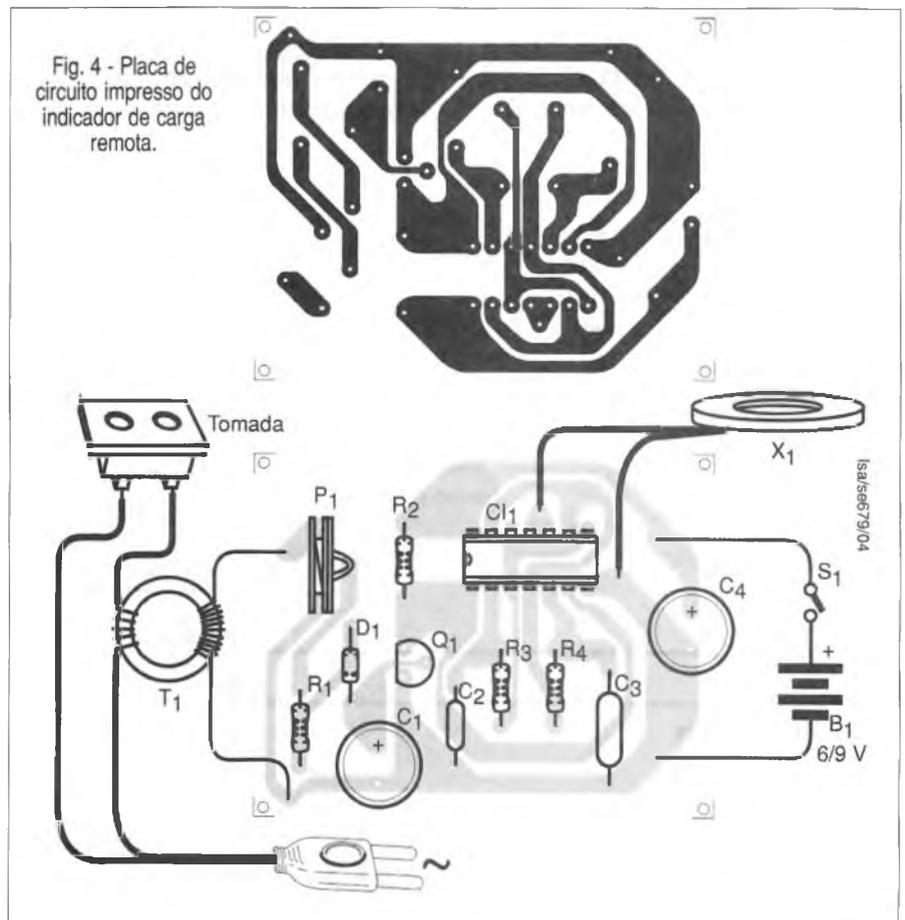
Placa de circuito impresso do indicador de carga remota.
